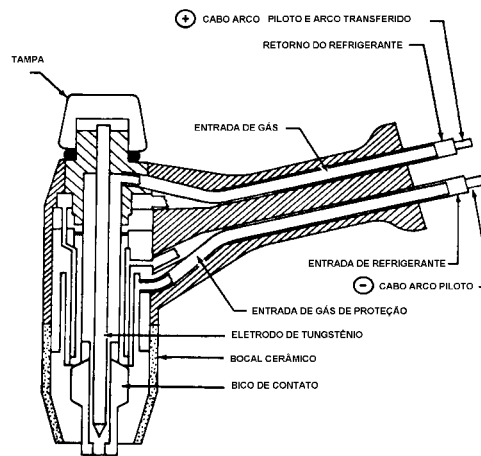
Detalhe para a tocha de soldagem PAW
